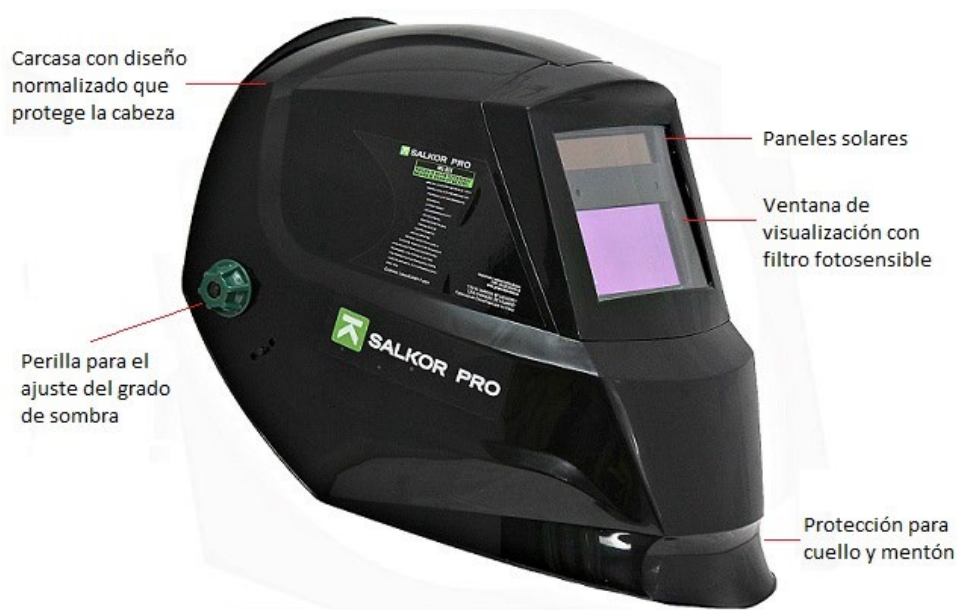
Máscara fotosensible para soldadura con sus componentes principales. [O-41]
